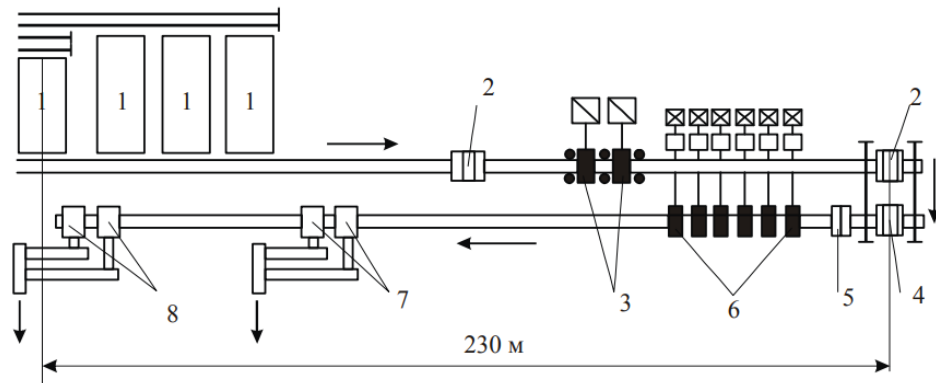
Схема зворотньо-напівбезперервного широкоштабового стану: 1 – нагрівальні печі; 2 – промічні перемотувальні пристрої; 3 – універсальні чорнові реверсивні кліти кварто; 4 – розмотувач; 5 – летючі ножиці; 6 – кліти кварто чистової групи; 7,8 – відповідно близькі і далекі моталки
